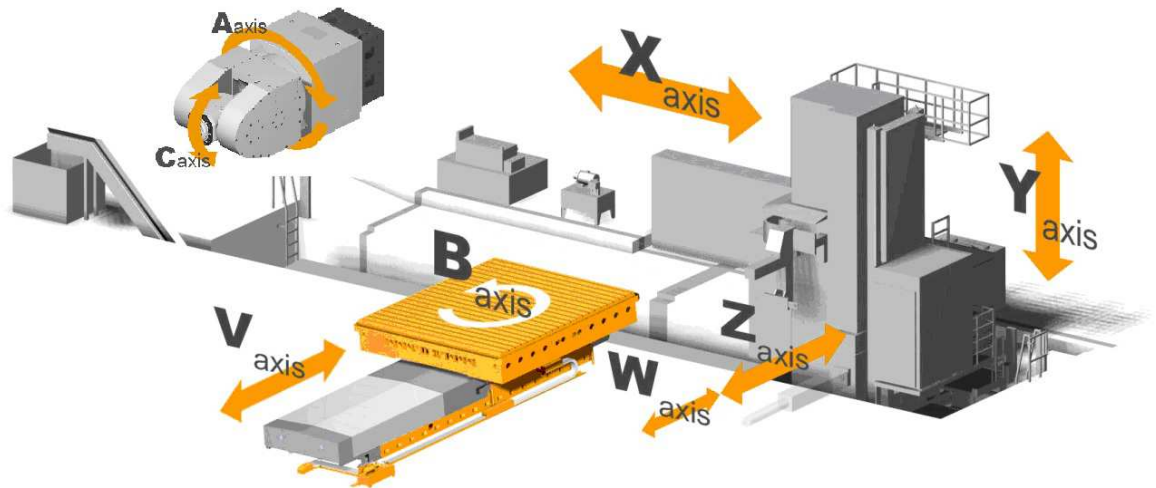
Pomůcka pro stanovení os souřadnicového systému [3]
